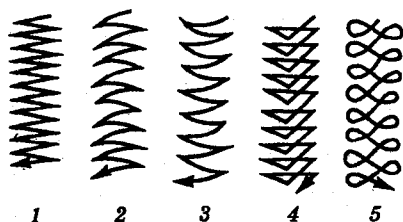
Колебательные движения электродом во время сварки
